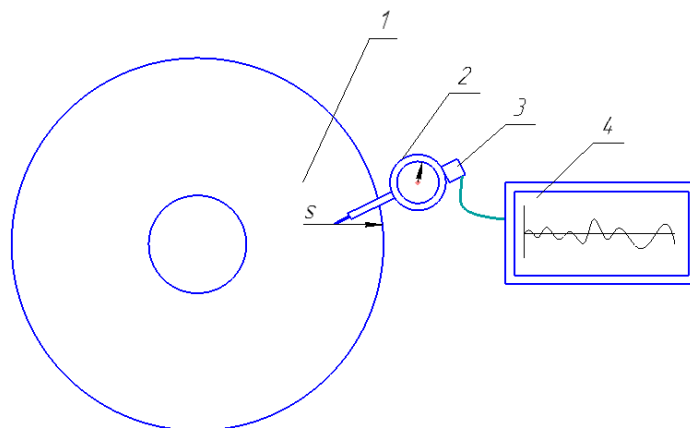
Схема прибора для определения рельефа тормозного диска:
